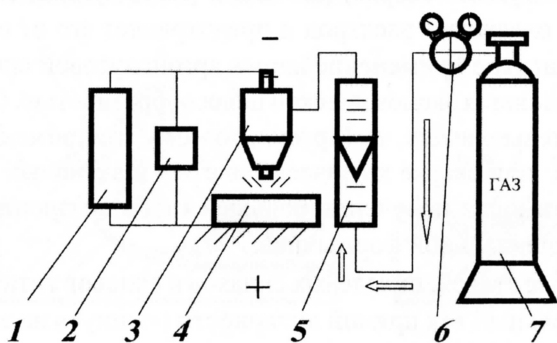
Схема установки для сварки неплавящимся электродом в защитном газе:
